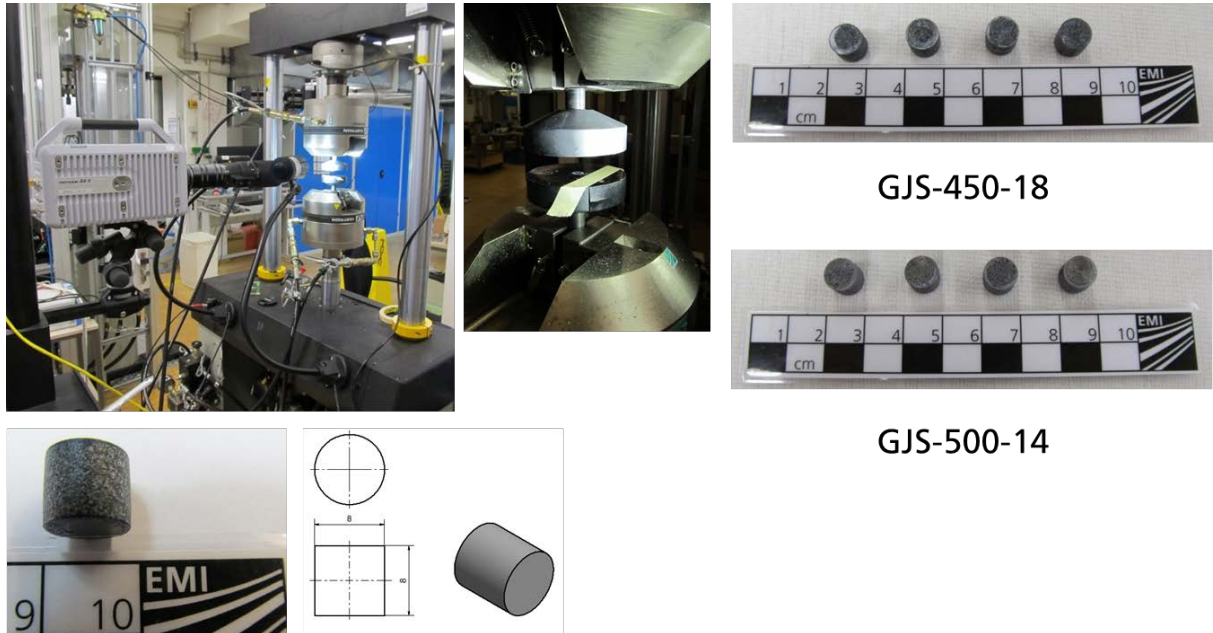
Versuchsaufbau auf hydraulischer Universalprüfmaschine, Prüfwerkzeug und Proben
